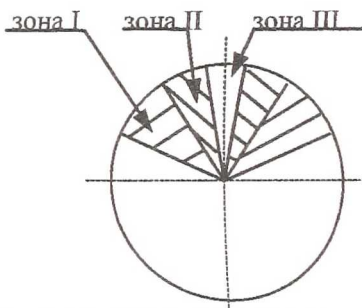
Расположение оксидных пленок на поверхности образца.
